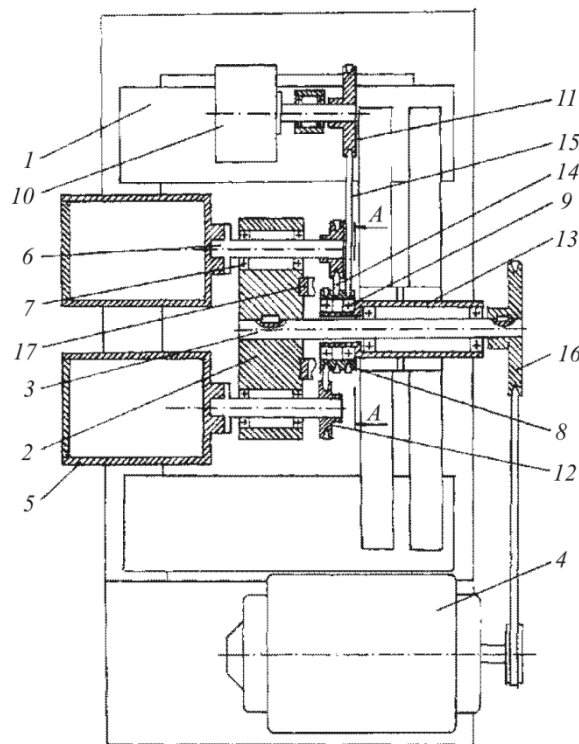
Схема планетарного гранулятора: 1 – рама; 2 – вило; 3 – основной вал; 4 – электродвигатель; 5 – формующий барабан; 6 – вал барабана; 7 – подшипники вала барабана; 8 – регулирующий вращение барабанов шкив; 9 – подшипники; 10 – тормозной механизм; 11 – шкив тормозного механизма; 12 – шкив барабана; 13 – корпус основного вала; 14 – ремень привода барабана; 15 – ремень тормозного механизма; 16 – шкив привода основного вала; 17 – стойка натяжителя ремня привода барабана
